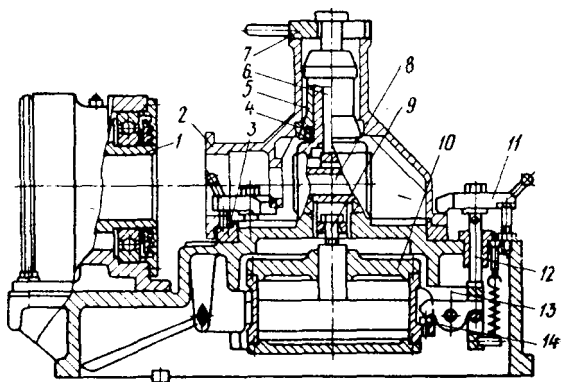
Приспособление с пневмозажимом к расточным станкам
